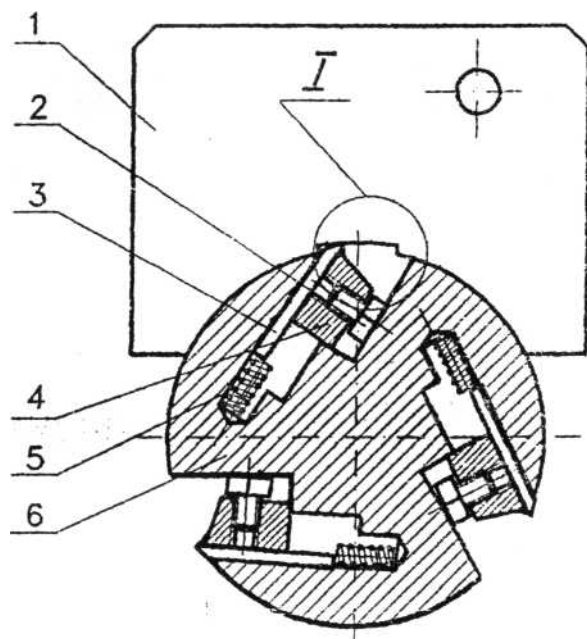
НАЛАДКА НОЖЕВОГО ВАЛА
